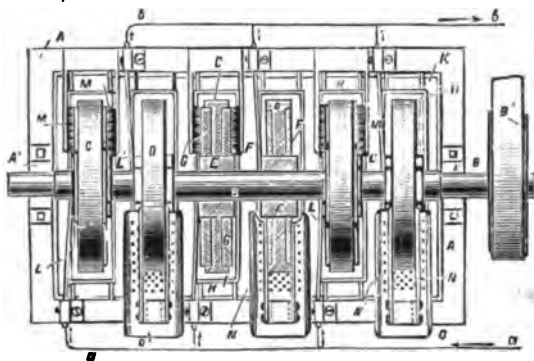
Apparat zur Silberaffination: Grundriss.
